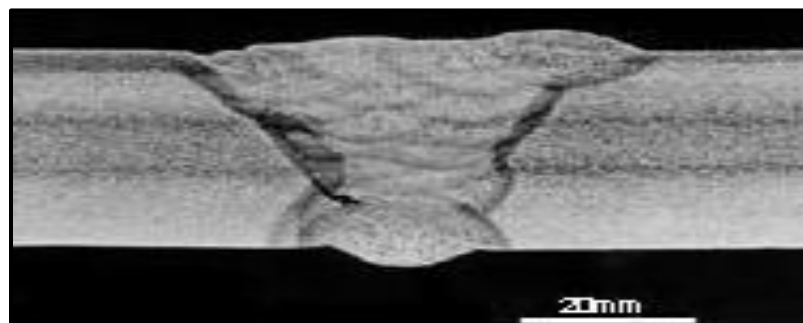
Manque de fusion dans le flanc de la soudure.
